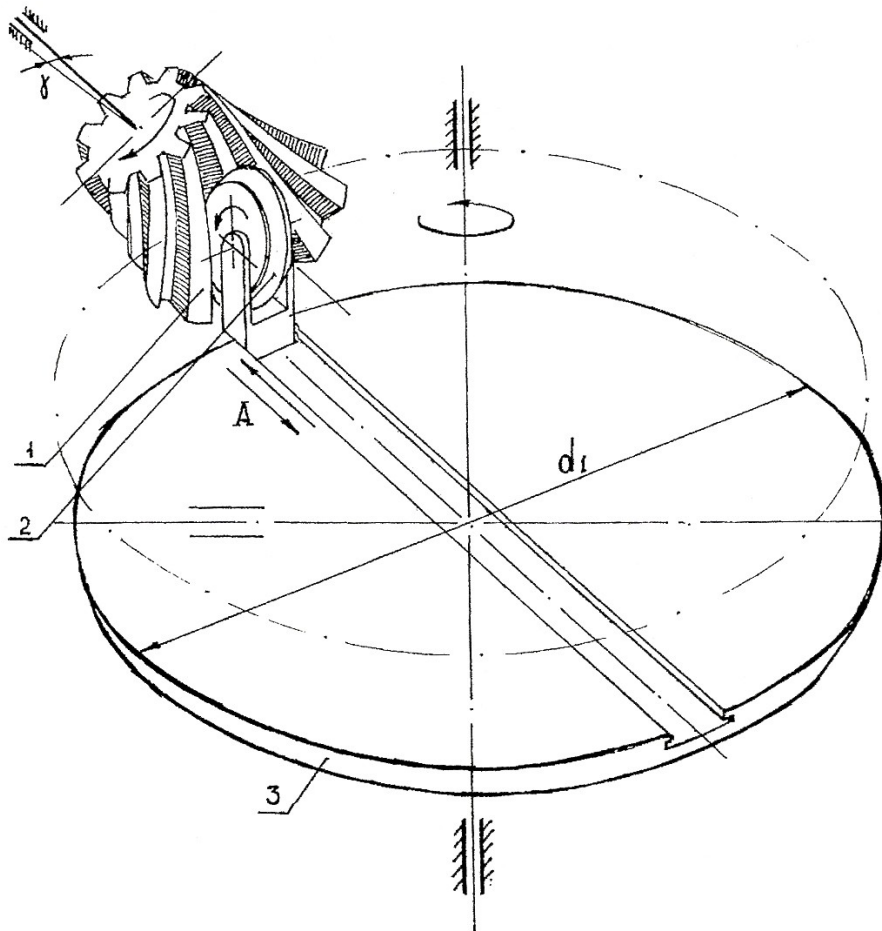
Способ изготовления гиперболоидных зубчатых колес
